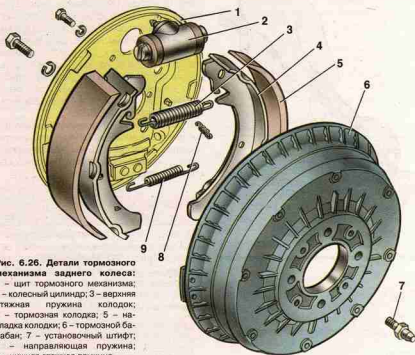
Детали тормозного механизма заднего колеса: 1 — шит тормозного механизма; 2 — колесный цилиндр; 3 — верхняя стяжная пружина колодок; 4 — тормозная колодка; 5 — накладка колодки; 6 — тормозной барабан; 7 — установочный штифт; 8 — направляющая пружина; 9 — нижняя стяжная пружина
